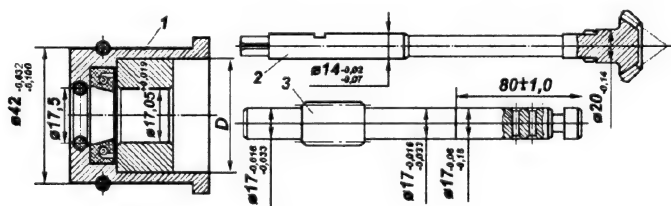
Посадочные размеры подшипника скольжения гребного вала и вала-шестерни
